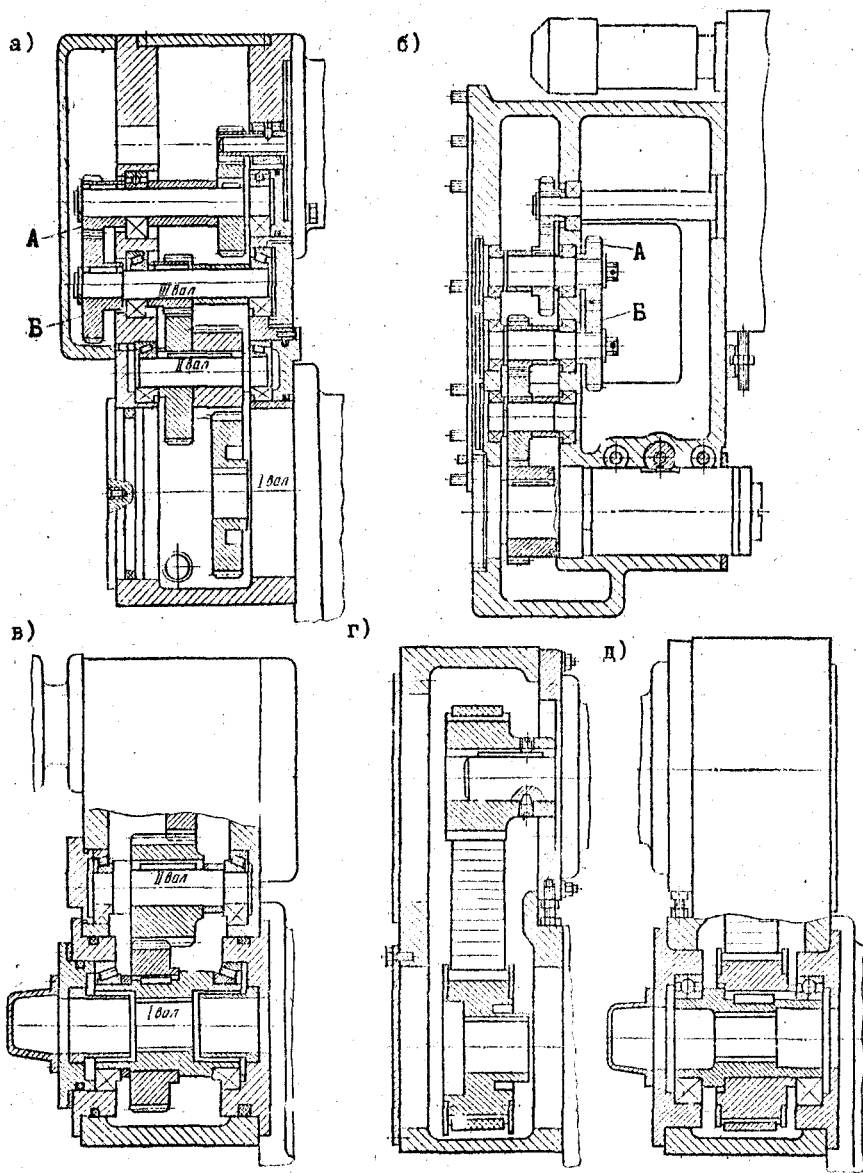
Приводы главного движения агрегатных станков с зубчатыми колесами (а, б, в) и с зубчатым ремнем (г, д)
